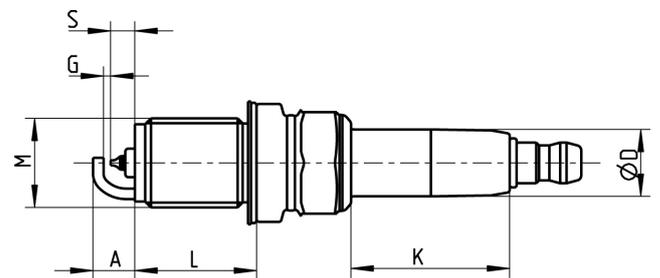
Dimensionen der Zündkerze Typ 6113B...
